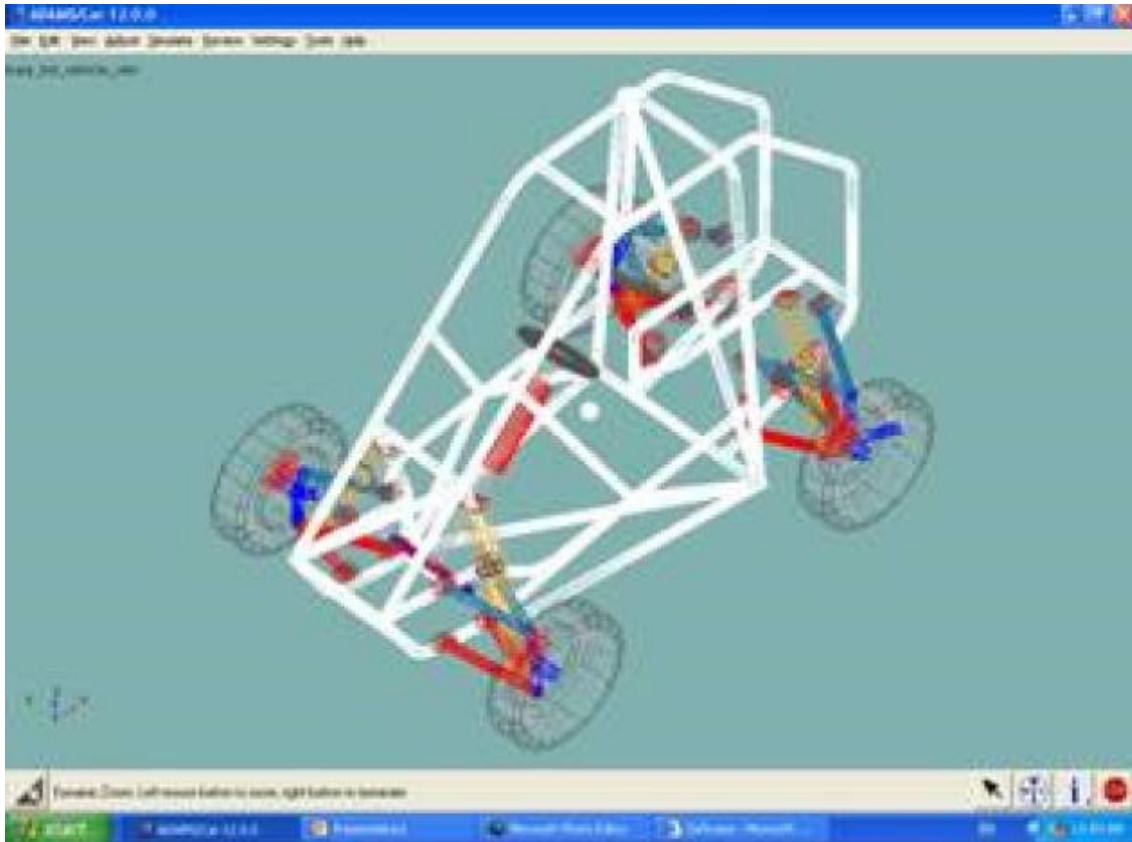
Diseño en ADAMS/Chassis.
